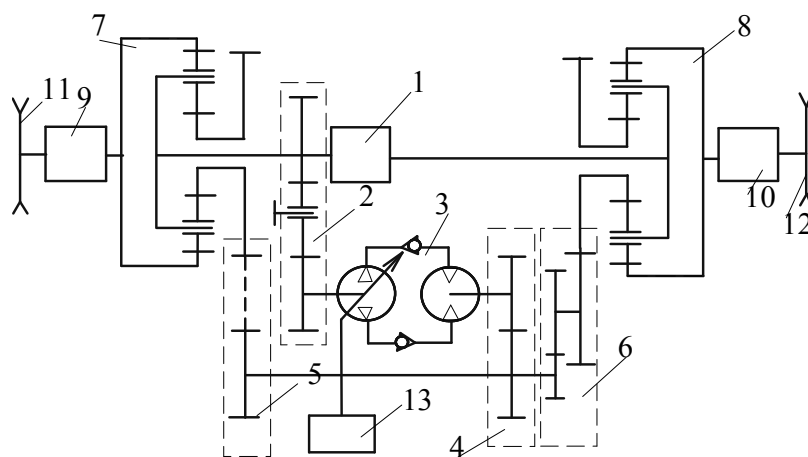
Кінематична схема двопоточного ГОМП: 1 – двигун; 2, 4, 5, 6-редуктори; 3 – ГОП; 7, 8 – диференціальні механізми; 9, 10-бортові коробки передач; 11, 12-ведучі колеса
